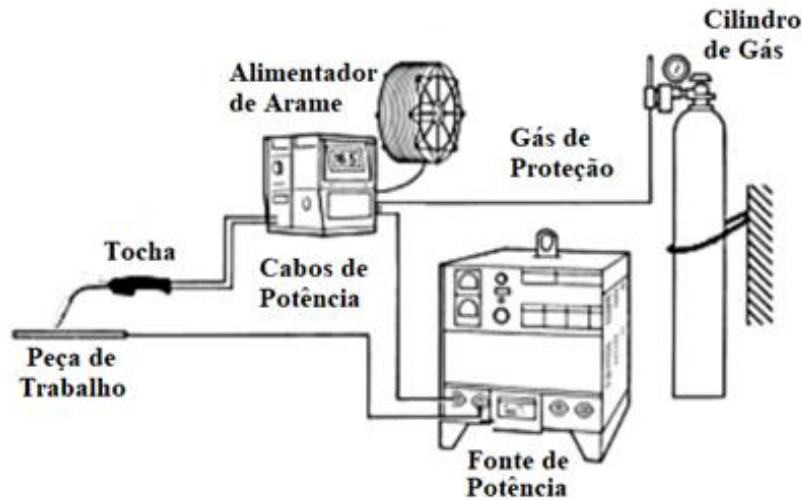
Componentes do equipamento de soldagem MAG [Gohr, 2002].
